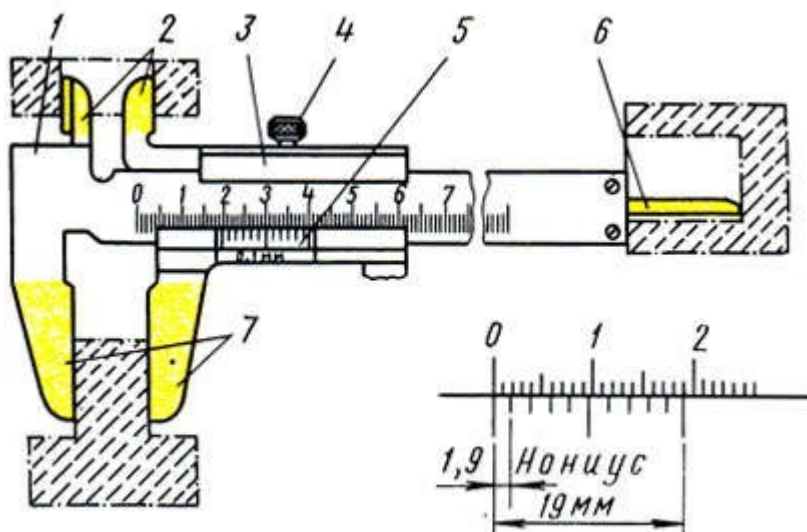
Штангенциркуль ШЦ-I: 1 - штанга, 2,7 - губки, 3 - подвижная рамка, 4 - зажим, 5 - шкала нониуса, 6 - линейка глубиномера
